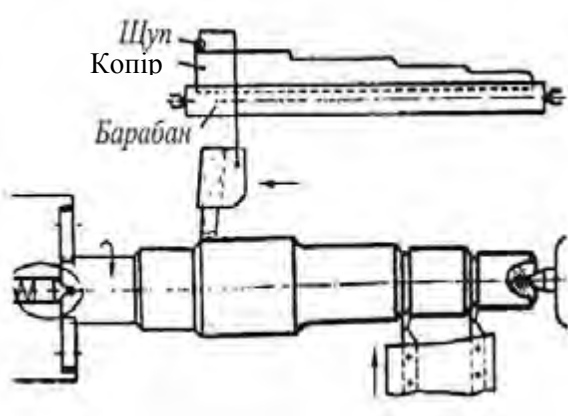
Схема оброблення заготовки на токарному гідрокопіювальному напівавтоматі
